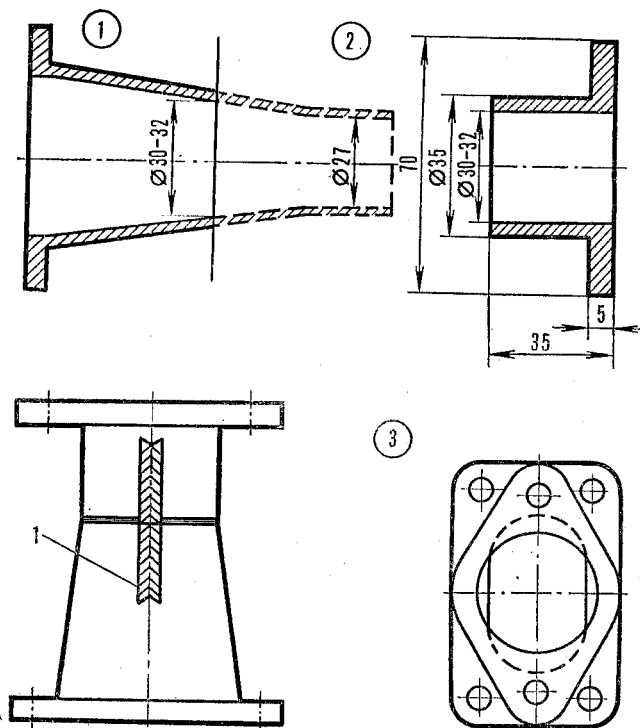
Впускной патрубок для карбюраторов К-194 и ИКОВ: 1 — стандартный патрубок; 2 — дополнительный фланец крепления карбюратора; 3 — готовый патрубок с ребром жесткости
